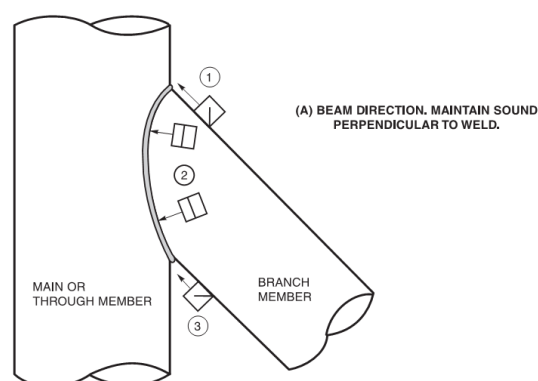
Escaneo de Unión Soldada en Conexiones T-Y-K
